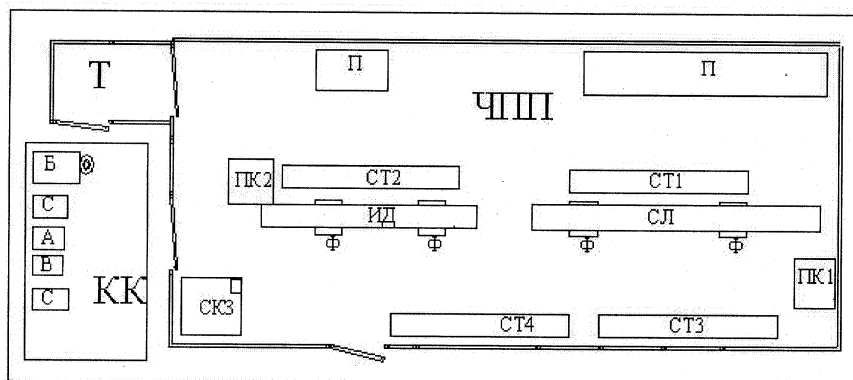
Схема расположения различного оборудования в чистом производственном помещении (ЧПП) и компрессорной комнате (КК). На схеме использованы следующие обозначения: СЛ – сборочная линия дрейфовых трубок, ИД – линия для измерения диаметра алюминиевых трубок, Ф – бетонные фундаменты, ПК1 и ПК2 – компьютеры, СТ1–СТ4 – стеллажи для укладки трубок, П – места для хранения комплектующих материалов, Т – тамбур для переодевания, Б – компрессор BAUER, С – компрессоры SECCATO, А – компрессор AIRMASTER, В - вакуумный насос М4
